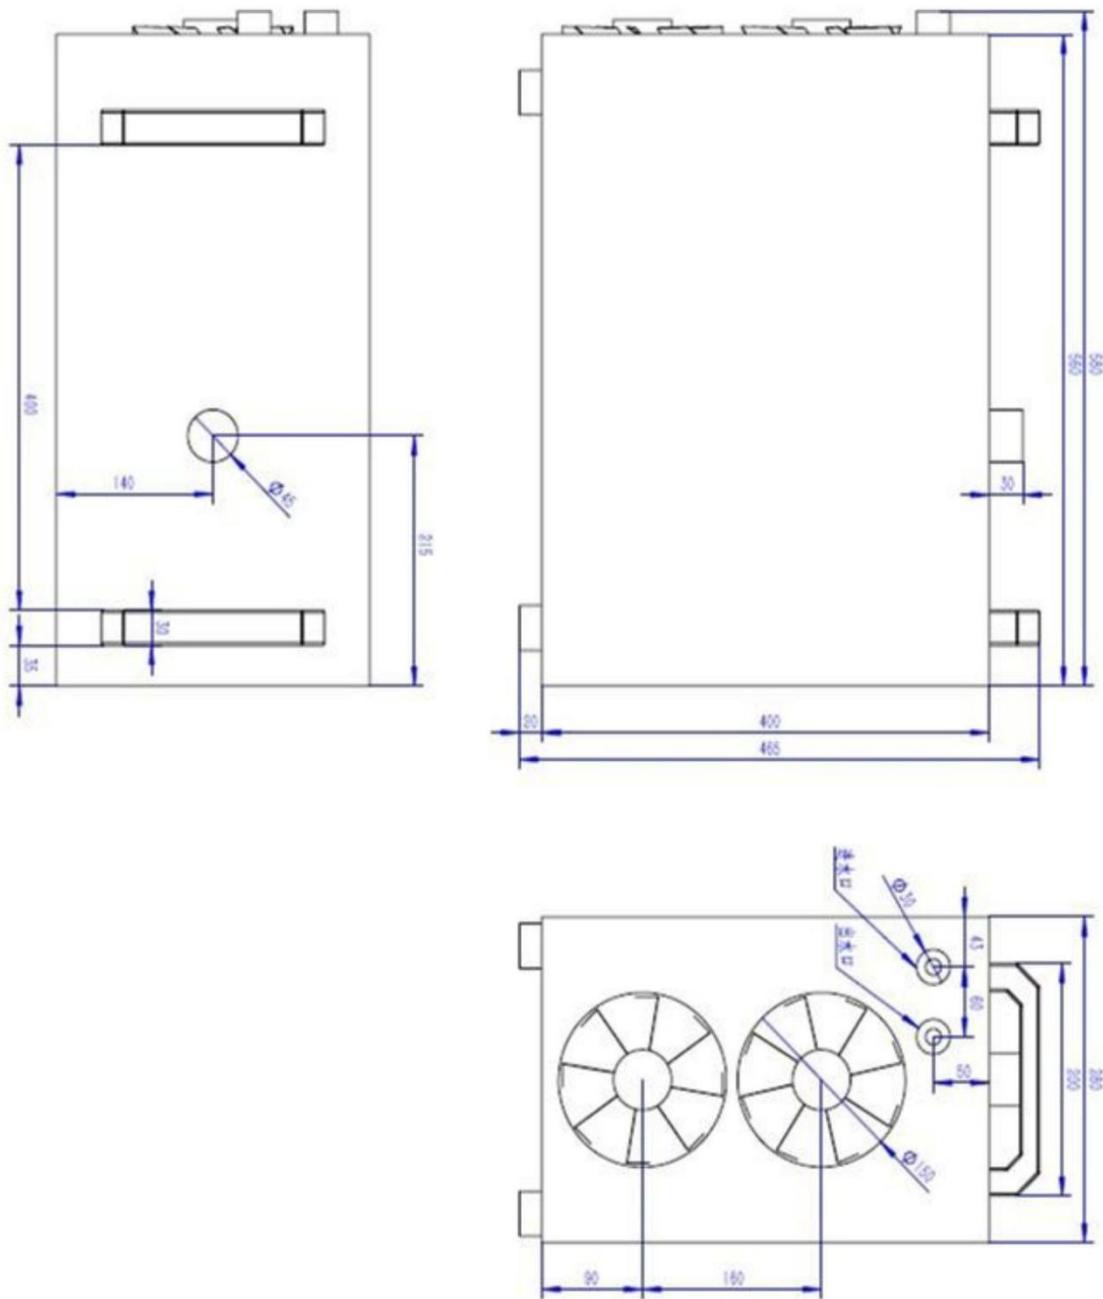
冷水机尺寸.9.4 Chiller Dimensions
